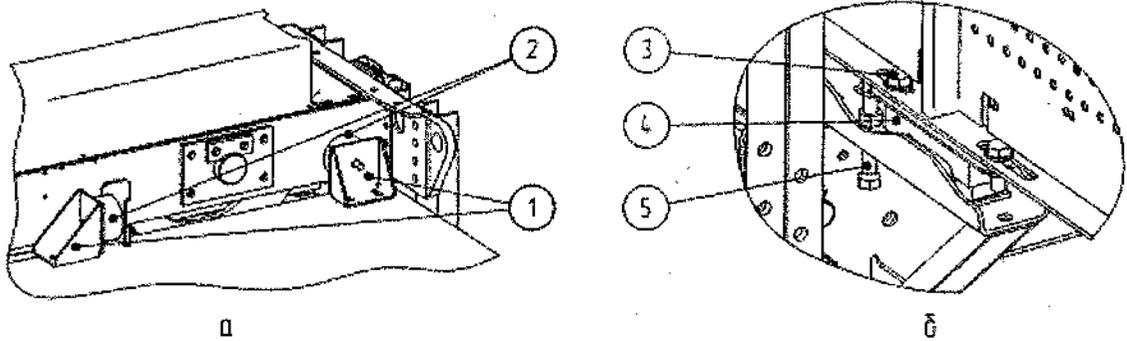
Схема крепления купе кабины: а) к верхней балке б) к нижней балке: 1 – Кронштейн крепления; 2 – амортизатор; 3 – болт крепления; 4 – датчик устройства взвешивающего; 5 – болт.
